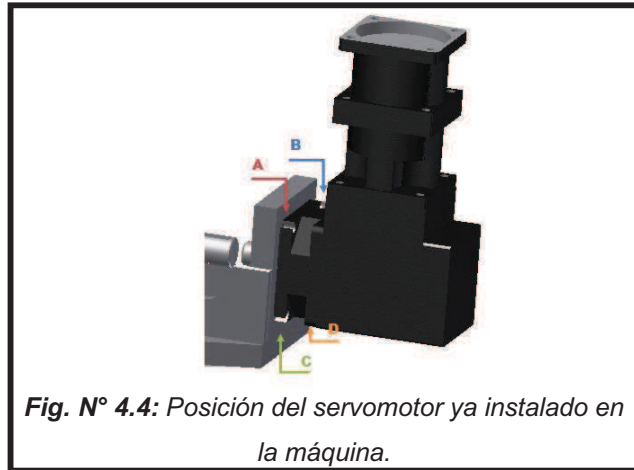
Posición del servomotor ya instalado en la máquina.
